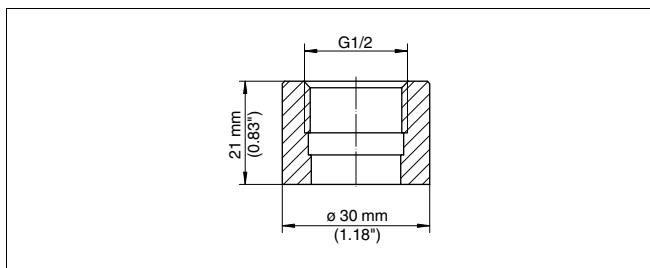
Medidas racor soldado G $\frac{1}{2}$  B según ISO 228-1 - tubería
